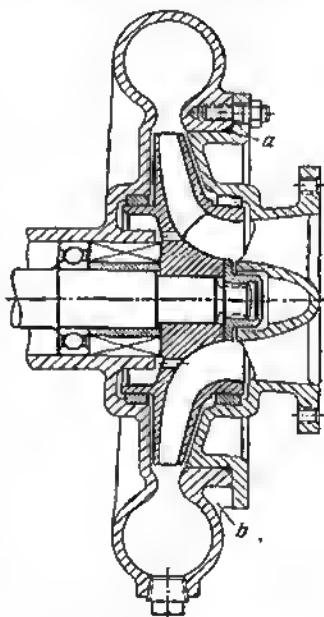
Dibujo de composición de la cavidad hidráulica de una bomba
